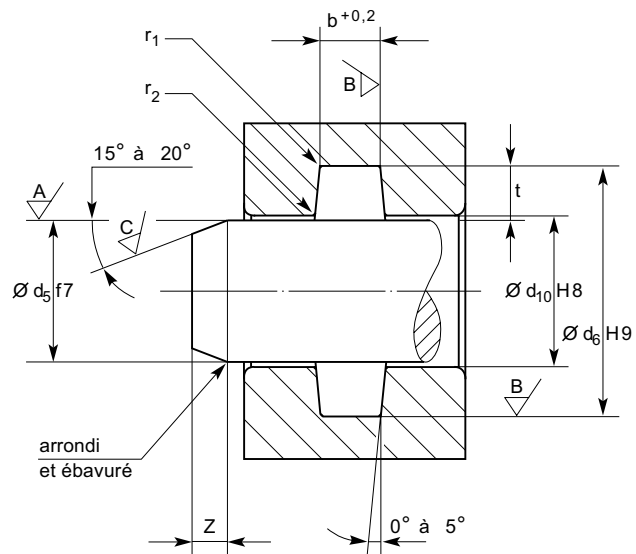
Joint de tige – hydraulique et pneumatique
